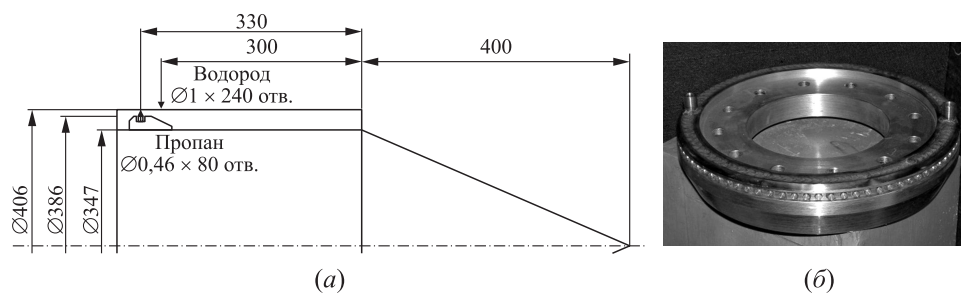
Схема установки в НДКС новой смешивательной головки для подачи жидкого топлива (размеры указаны в миллиметрах) (а) и фотография смешивательной головки (б)
